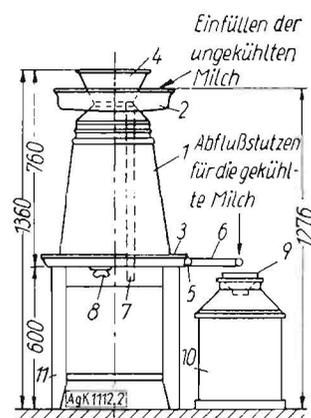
Milchkühler des Unions-Forschungsinstituts. 1 Kühler; 2 Gefäß zum Einschütten der Milch; 3 Sammler für die gekühlte Milch; 4 Trichter zum Einlegen von Eis; 5 Verbindungsstück zwischen Hahn und Sammler; 6 Hahn; 7 Rohr für den Abfluß des Tauwassers; 8 Abflußrohr für die Leerung des Kühlers; 9 Filter für die gekühlte Milch; 10 Kanne zur Aufnahme der gekühlten Milch; 11 Podest zum Aufstellen des Kühlers
